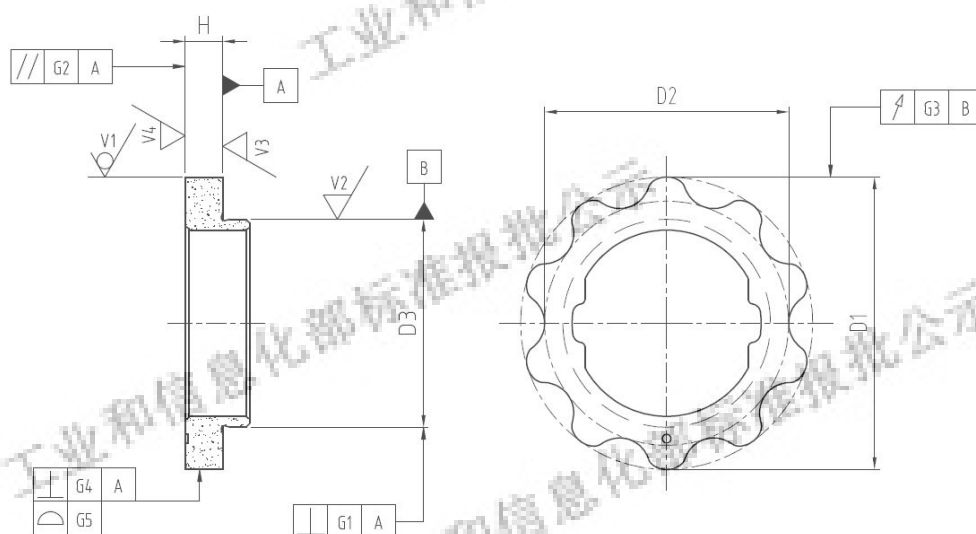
外圆轴颈定位式内转子尺寸、几何公差及表面粗糙度标注示意图
